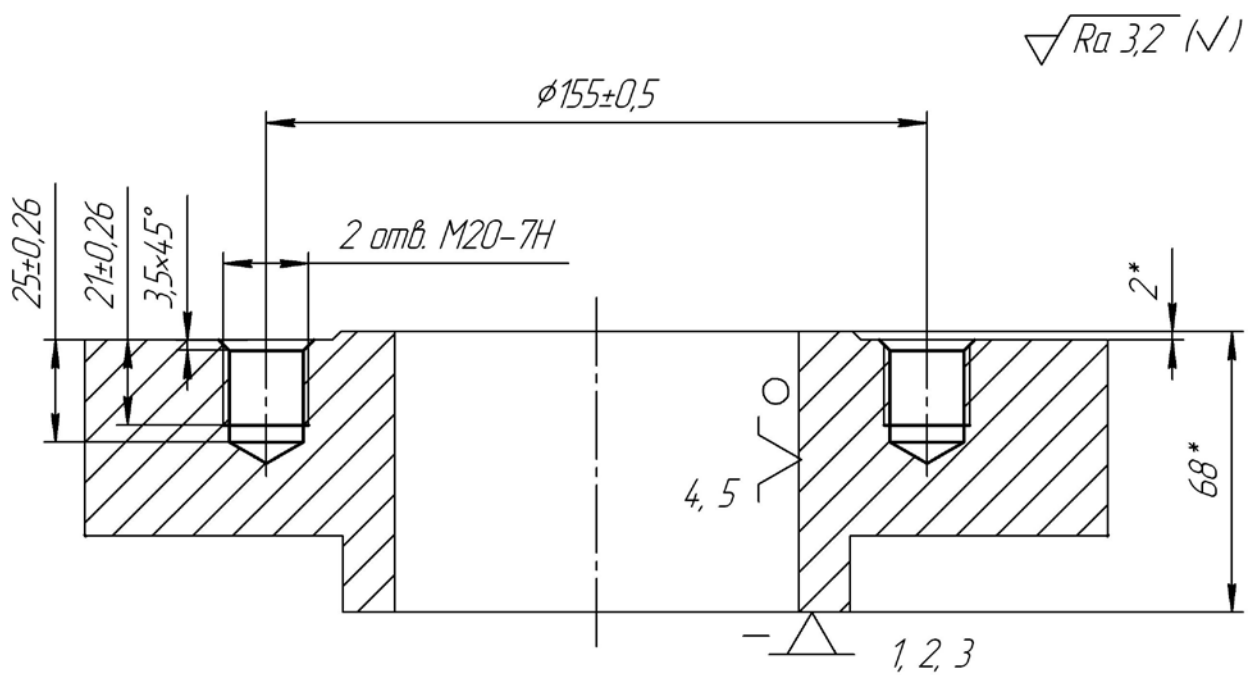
Альтернативна схема базування заготовки на операції 025 свердлильній з ЧПК
